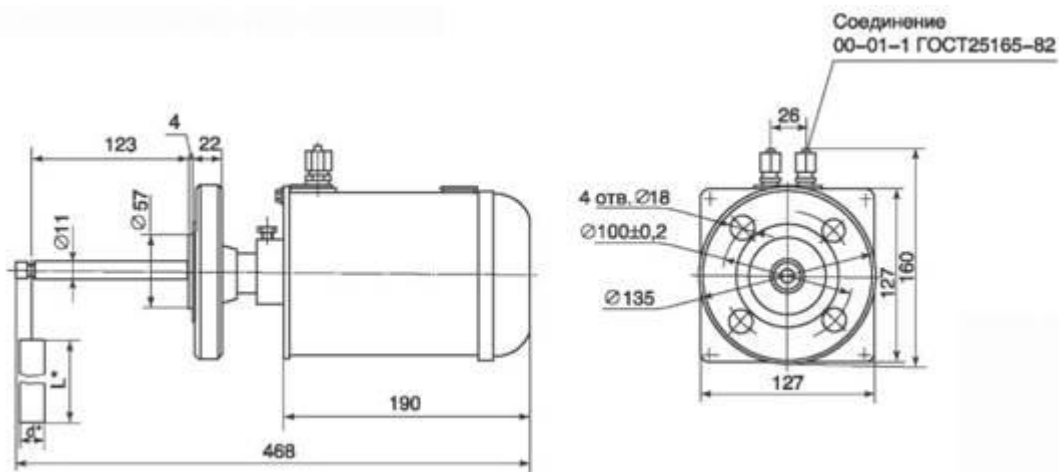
Габаритные, установочные и присоединительные размеры преобразователей ПИУП-М-11, ПИУП-М-21
